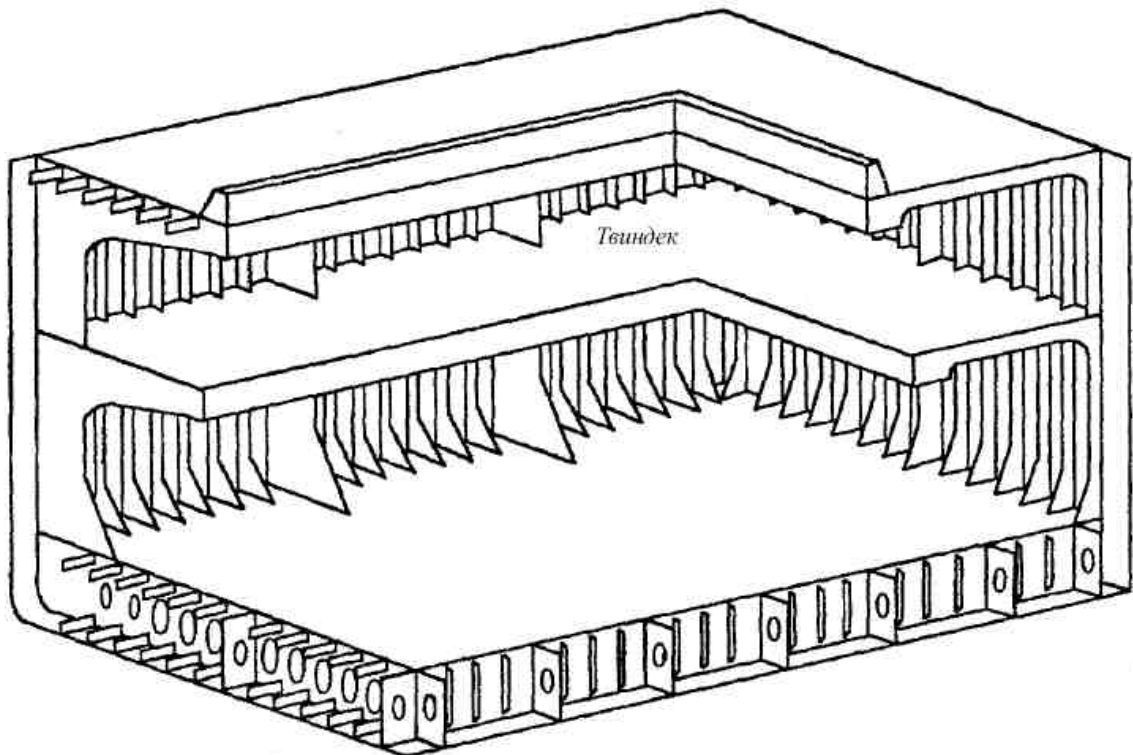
Схема конструкции отсека двухпалубного сухогруза со смешанной системой набора корпуса
